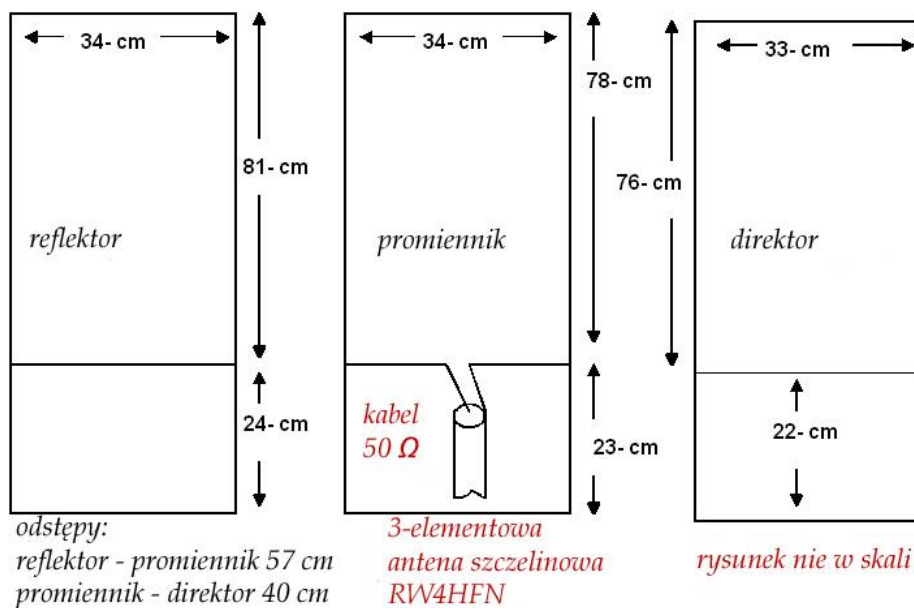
Konstrukcja anteny z płaskownika
